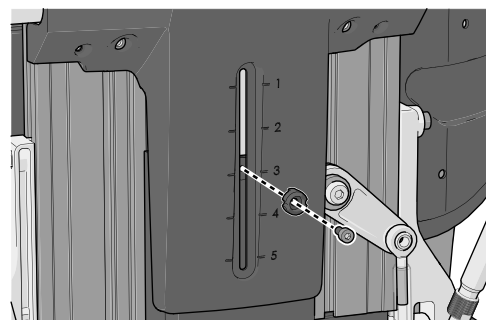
Der Kunststoffknopf ist mit einer Schraube befestigt.
